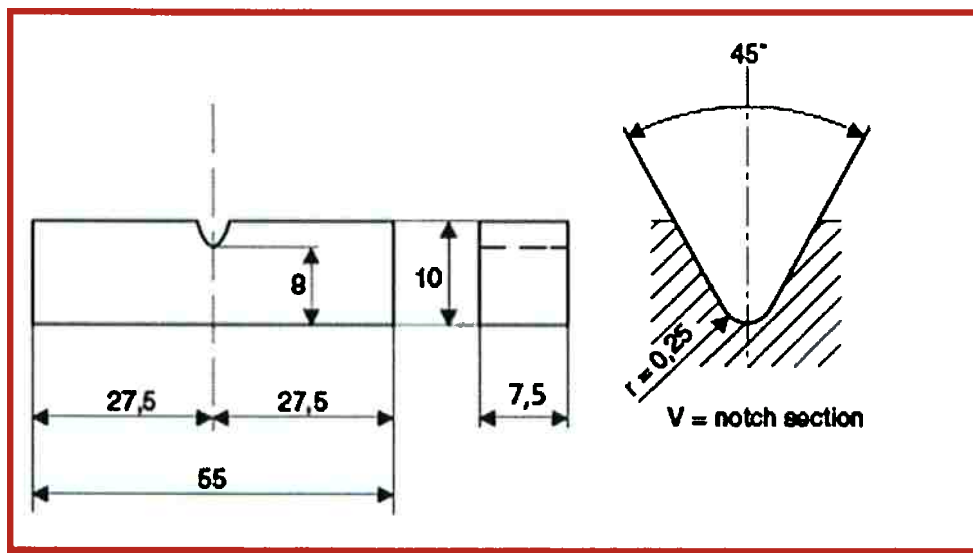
Dimensões do corpo de prova sub-size (mm) para o ensaio de impacto Charpy.
